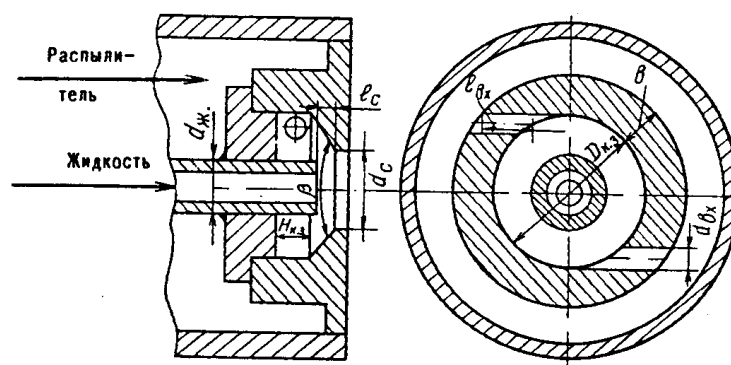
Схема пневматической (паровой) форсунки вихревого типа
